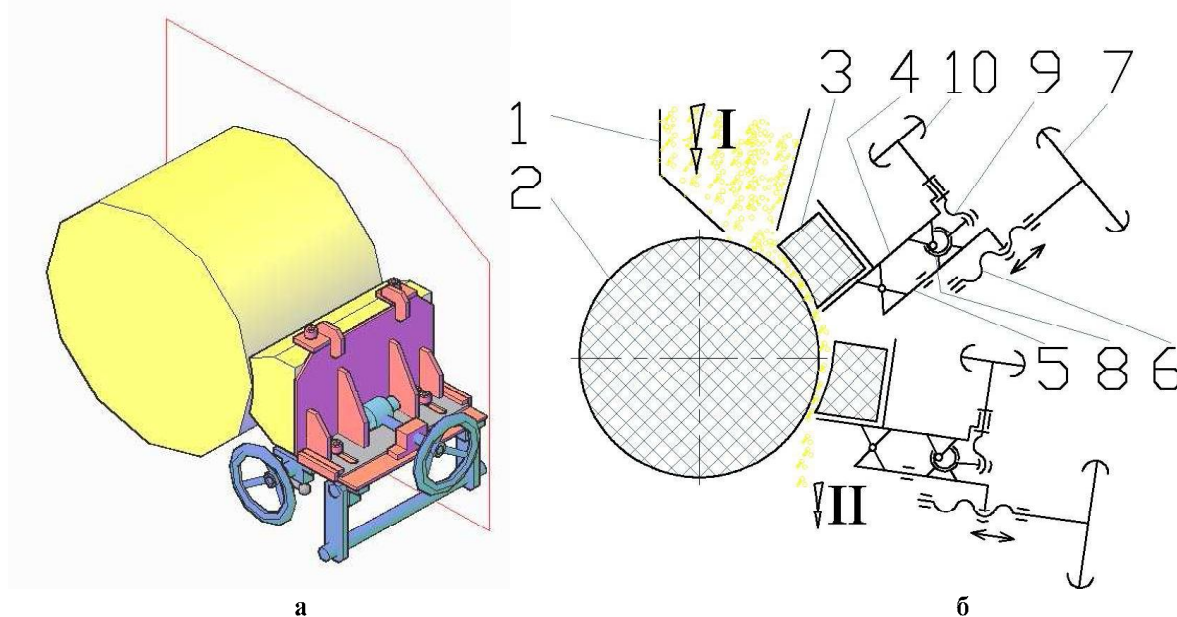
Схема нового установочного механизма деки (а) и схема вальцедекового станка с двумя деками (б)
